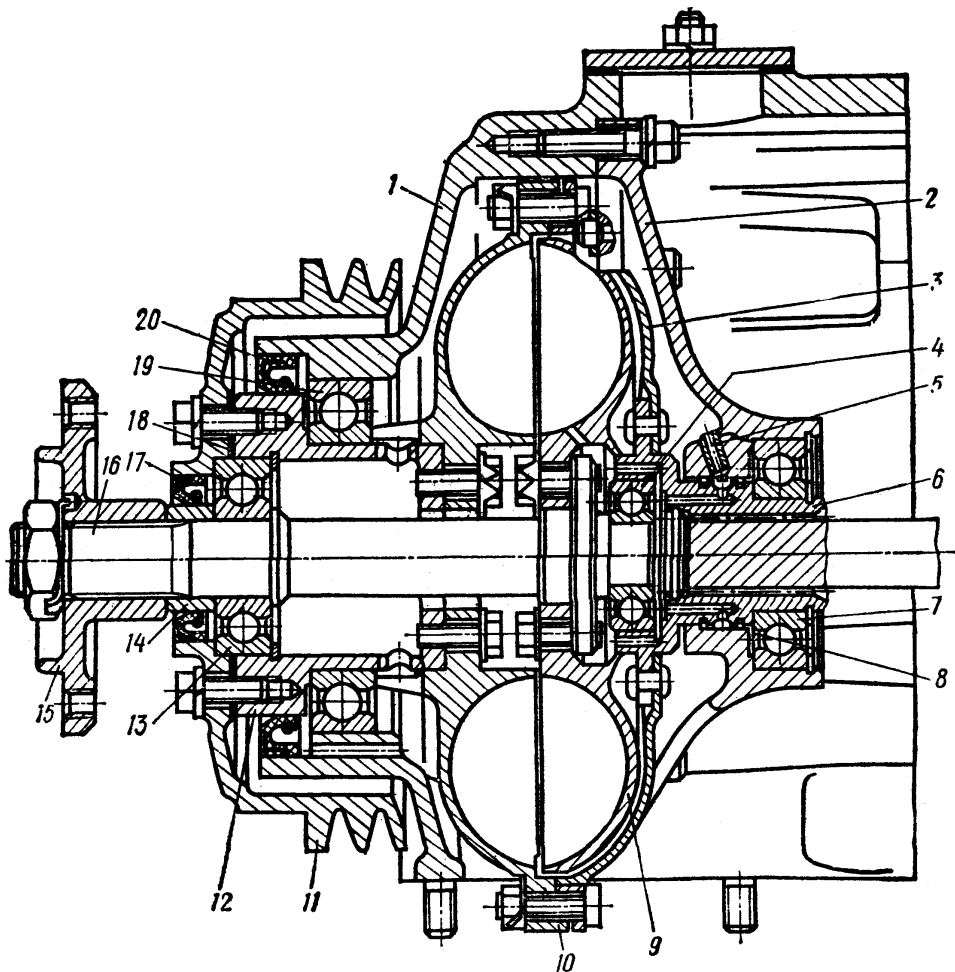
Гідромуфта приводу вентилятора двигуна ЯМЗ-740:
